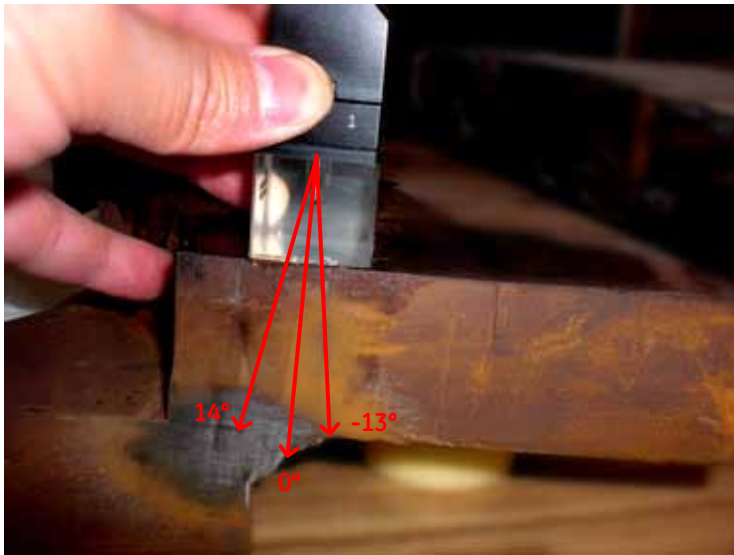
Posición del transductor abarcando el área de la soldadura.
